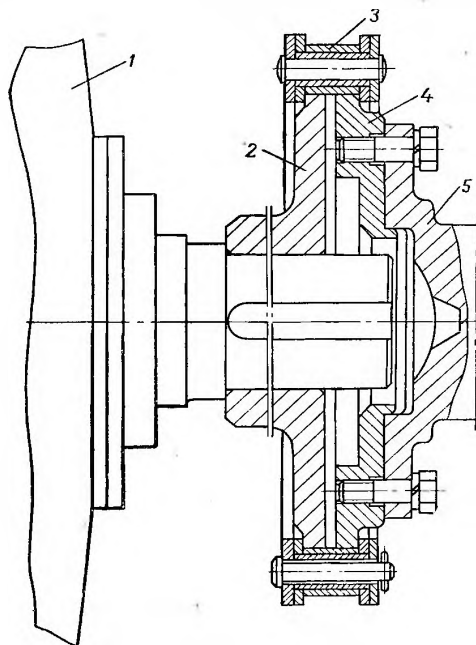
Соединение электродвигателя механизма передвижения с коробкой перемены передач экскаватора ЭТР231
